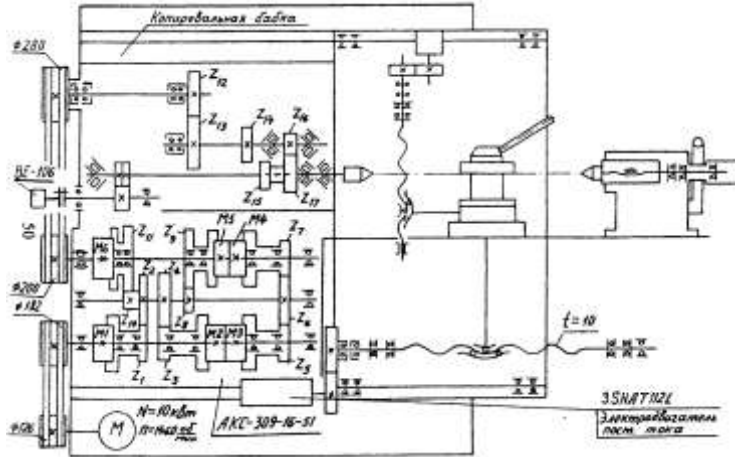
Кинематическая схема привода станка с ЧПУ 16К20Т1
